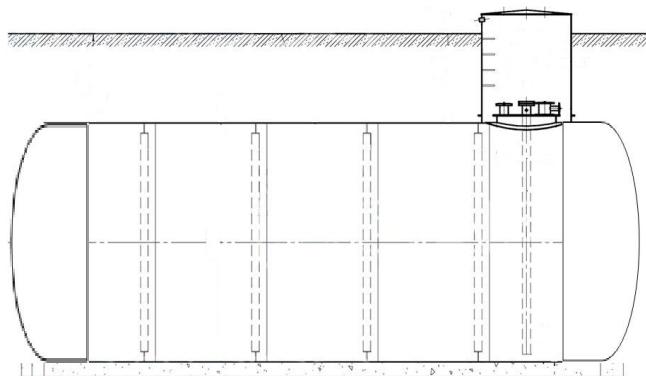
Эскиз конструкции резервуара РГС-63 № 58563
